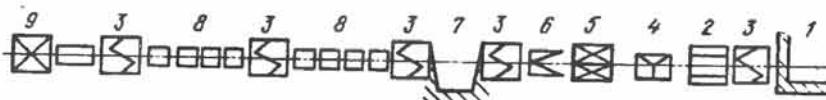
Схема участка сварки заготовок на мелкосортном стане 250 бесконечной прокатки:
